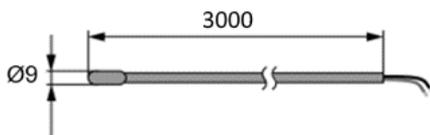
Abmessungen externer Fühler des Anschluss-Sets (Angaben in mm)
